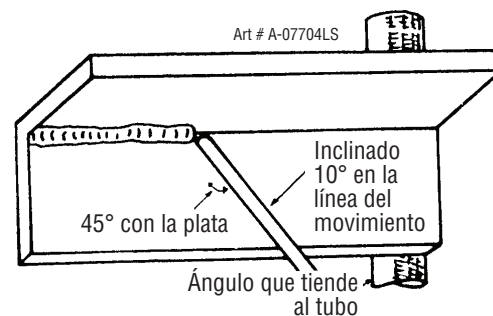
Soldadura de perfil en ángulo de posición en elevación
